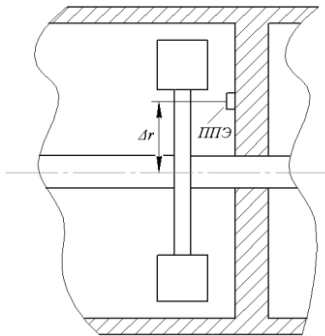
Расположение доплеровского преобразователя в корпусе турбоагрегата для определения форм колебаний диска
